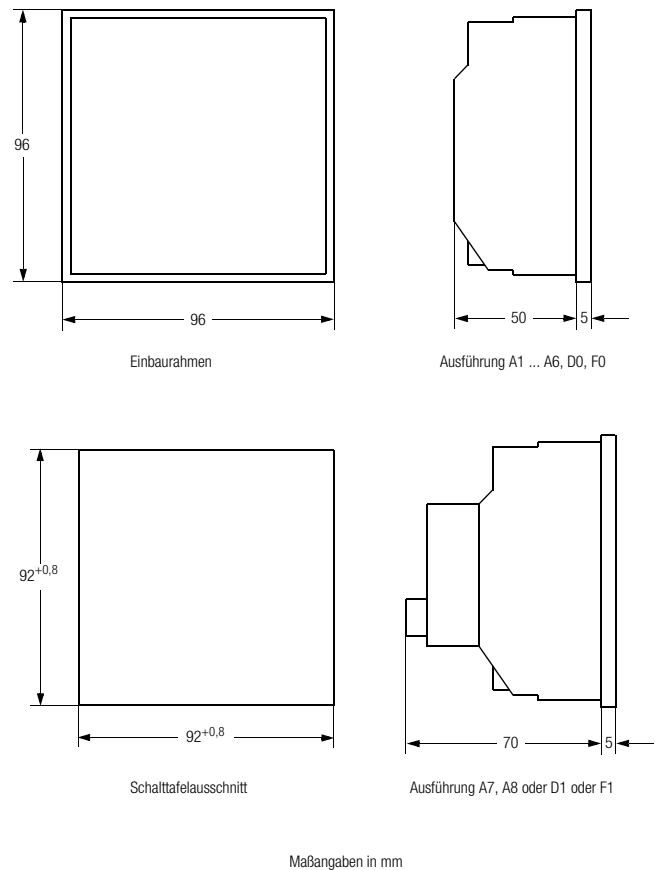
, Gehäuseabmessungen und Schalttafelaustritt
